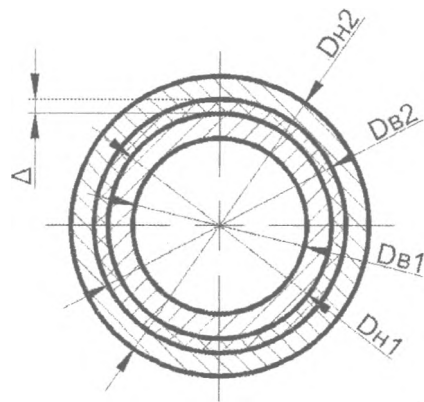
Поперечное сечение двухслойного гидроцилиндра
